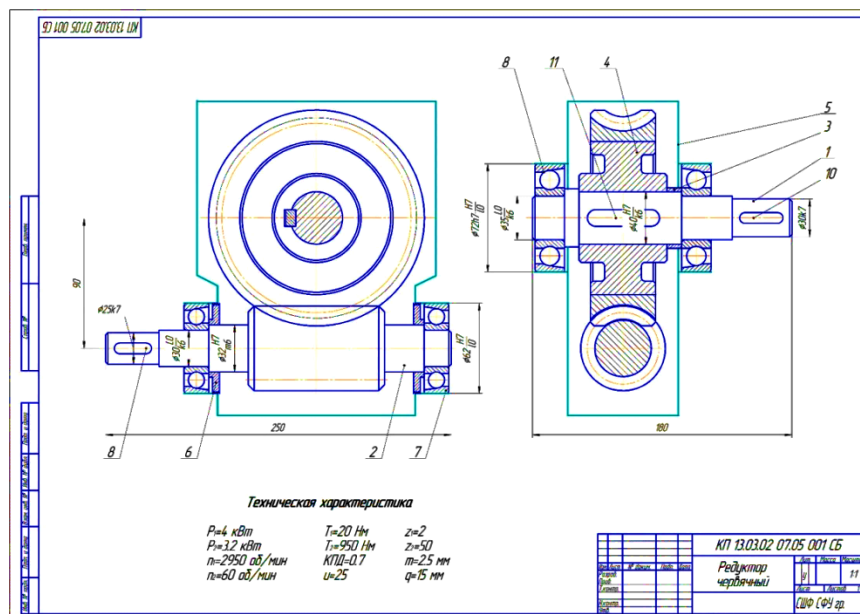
Сборочный чертеж «Редуктор червячный»
